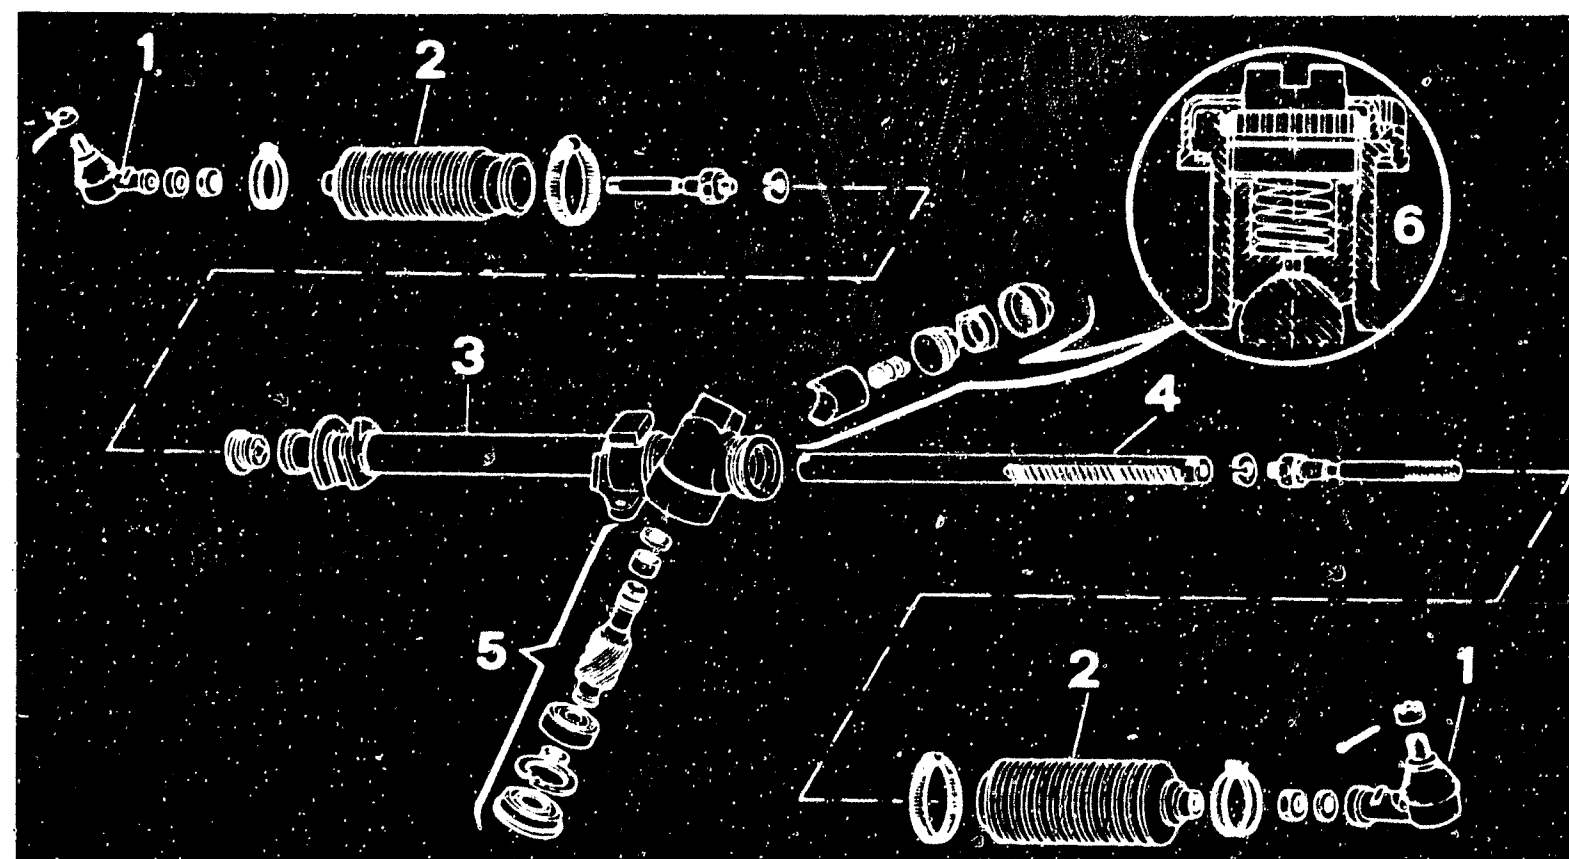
Mechanische Zahnstangenlenkung: 1 Spurstangengelenk – 2 Manschetten – 3 Lenkgehäuse – 4 Zahnstange – 5 Ritzel mit Lagerung – 6 Druckstück mit Einstellschraube.
